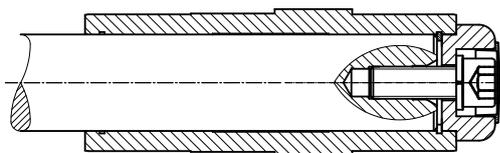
Установка редуктора на вал без буртика с помощью крепежного элемента
